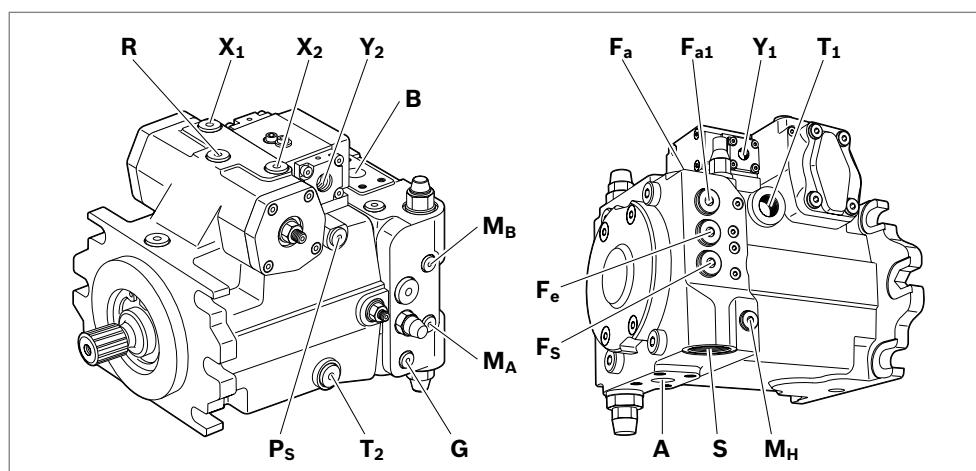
Vue d'ensemble des raccords A4VG, dimension nominale 71 à 180
